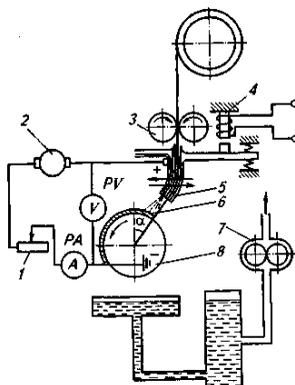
Принципиальная схема установки для вибродуговой наплавки:
